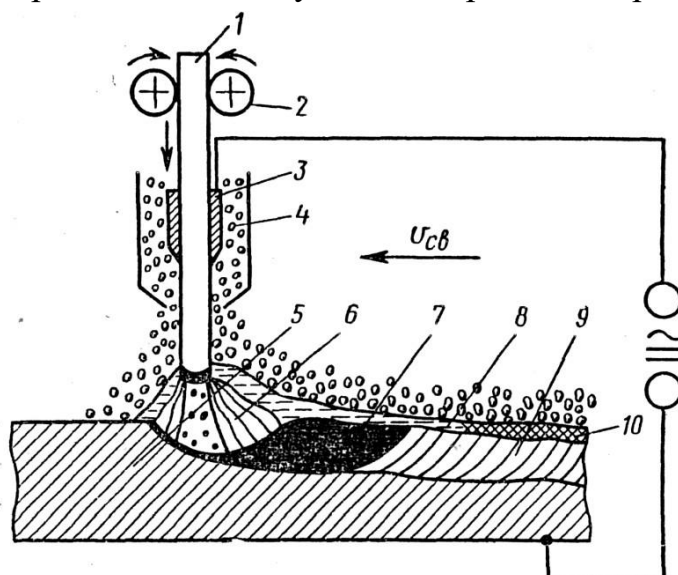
Схема автоматичного зварювання під флюсом:
